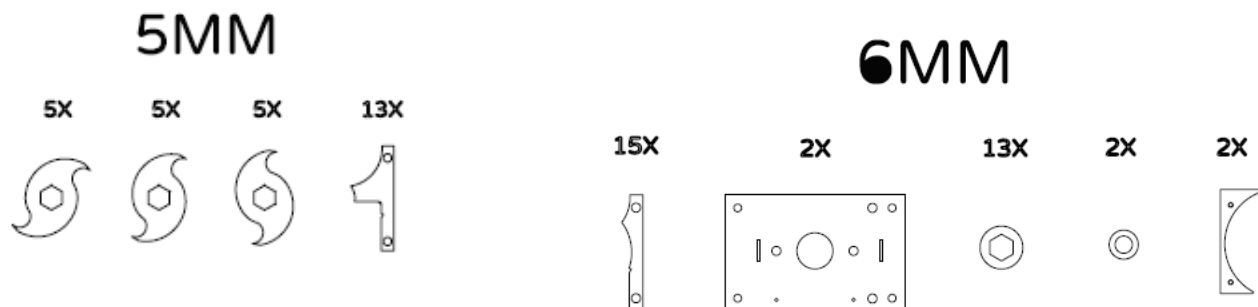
Ножи шредера Рисунок 6 – Высокопрочные детали шредера
